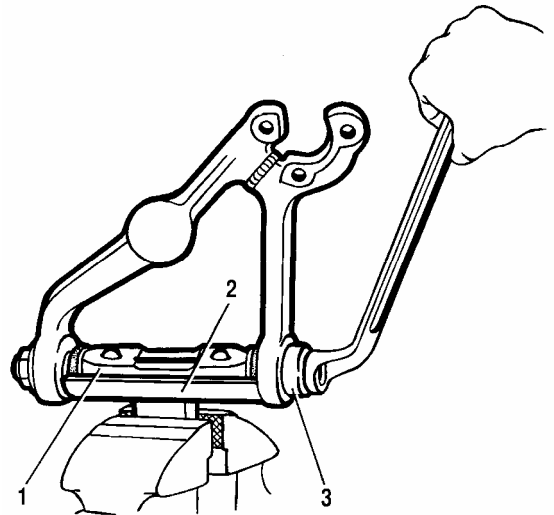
Выпрессовка шарниров верхнего рычага:
